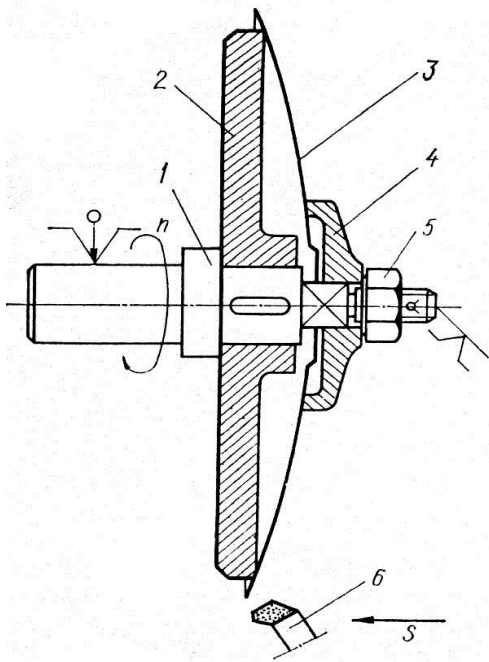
Схема заточування диска на токарно-гвинторізному верстаті різцем:
